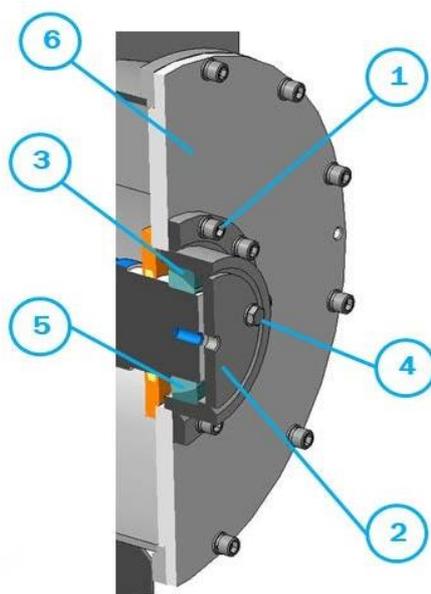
Схема демонтажа подшипника задней опоры.
